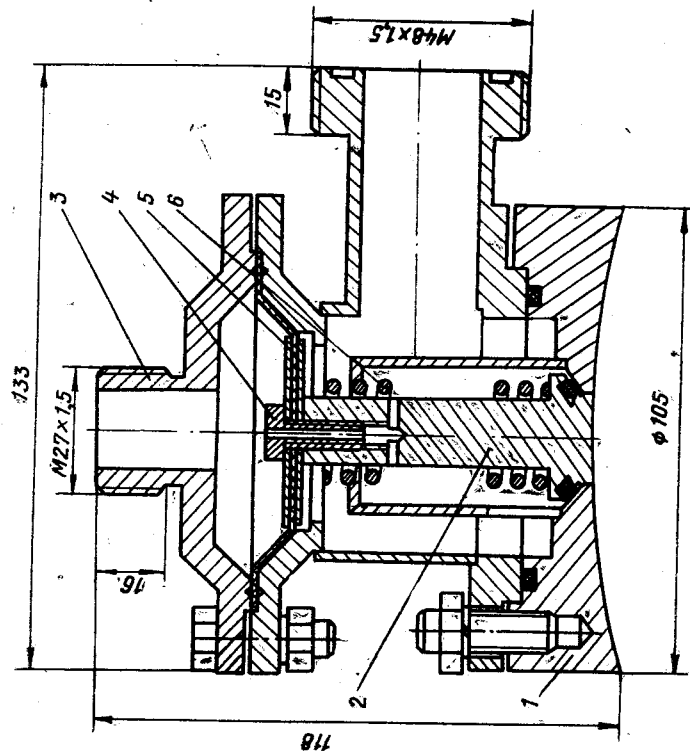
Насадок клапанный мембранный НКМ (черт. ЭС519.000, ВНИИПО):
